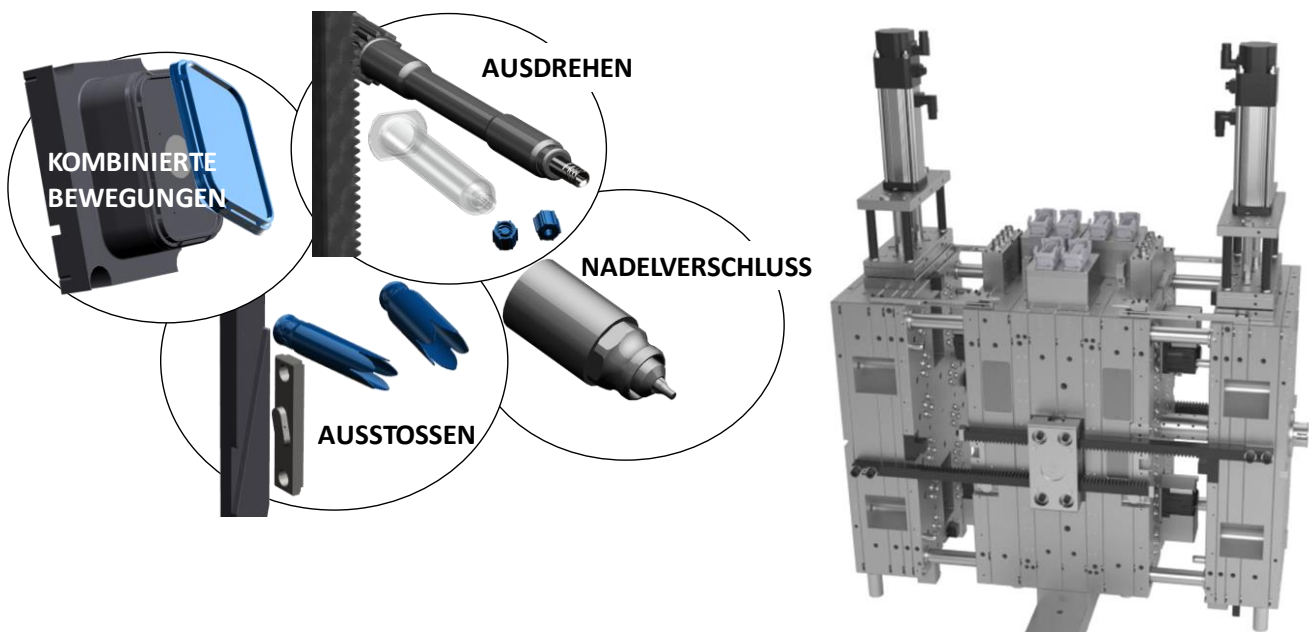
Lösungen für elektrische Werkzeugbewegungen / 72+72fach Etagenwerkzeug für Verschlusskonus
